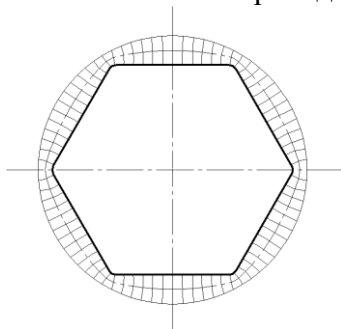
Контур поперечного сечения внутренней поверхности заготовки 1 (тонкая линия), промежуточного перехода 2 (штрих-пунктир) и готовой трубы 3 (толстая линия). Наружные контуры заготовки и готовой трубы не показаны
